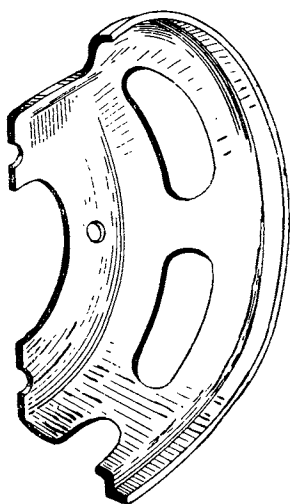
Штампованный диффузордержатель (ГДД-157)
